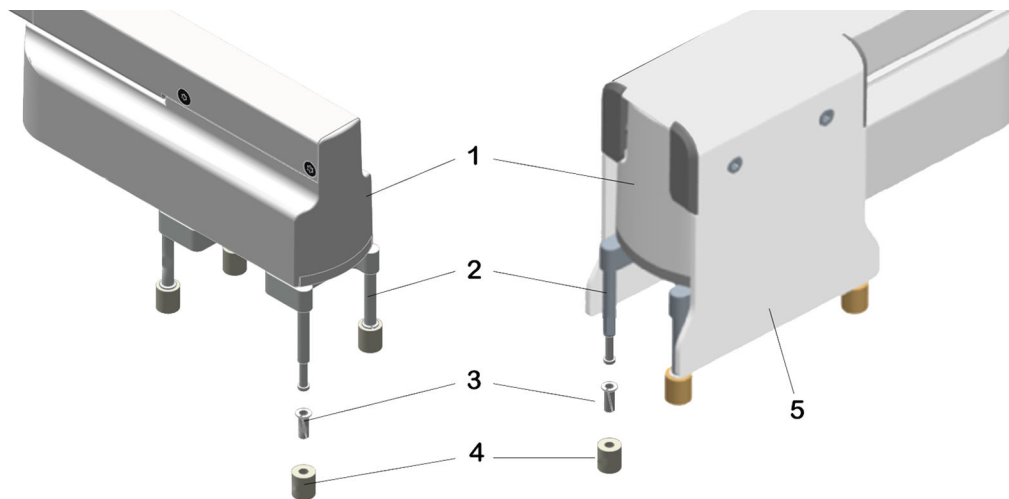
Remplacement du caoutchouc et de la douille coulissante d'un doigt
